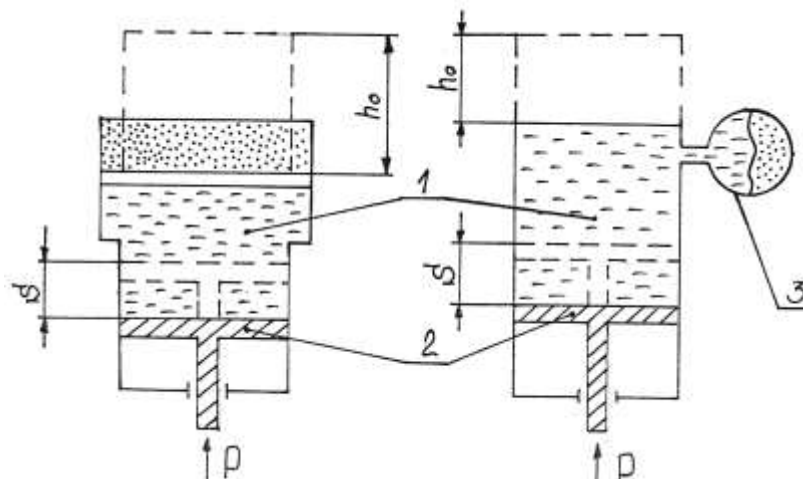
Телескопический упругий элемент с одной ступенью давления: 1 – рабочий цилиндр; 2 – поршень; 3 – дополнительный резервуар; S – ход поршня от начального положения; h – приведенная высота столба газа; P – сила, действующая на шток
